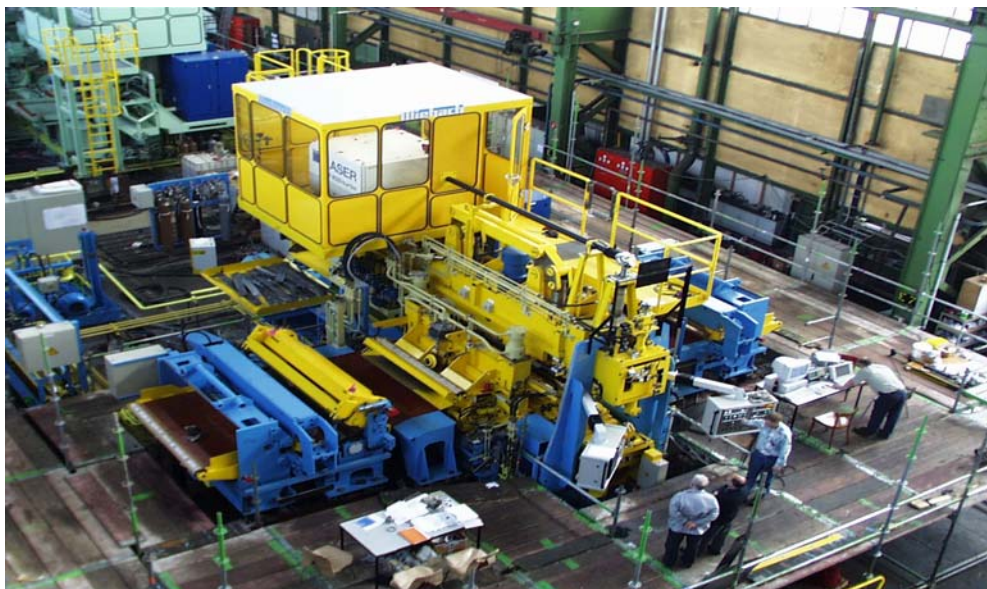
Máquina de solda a laser da Miebach.⁽²⁾
